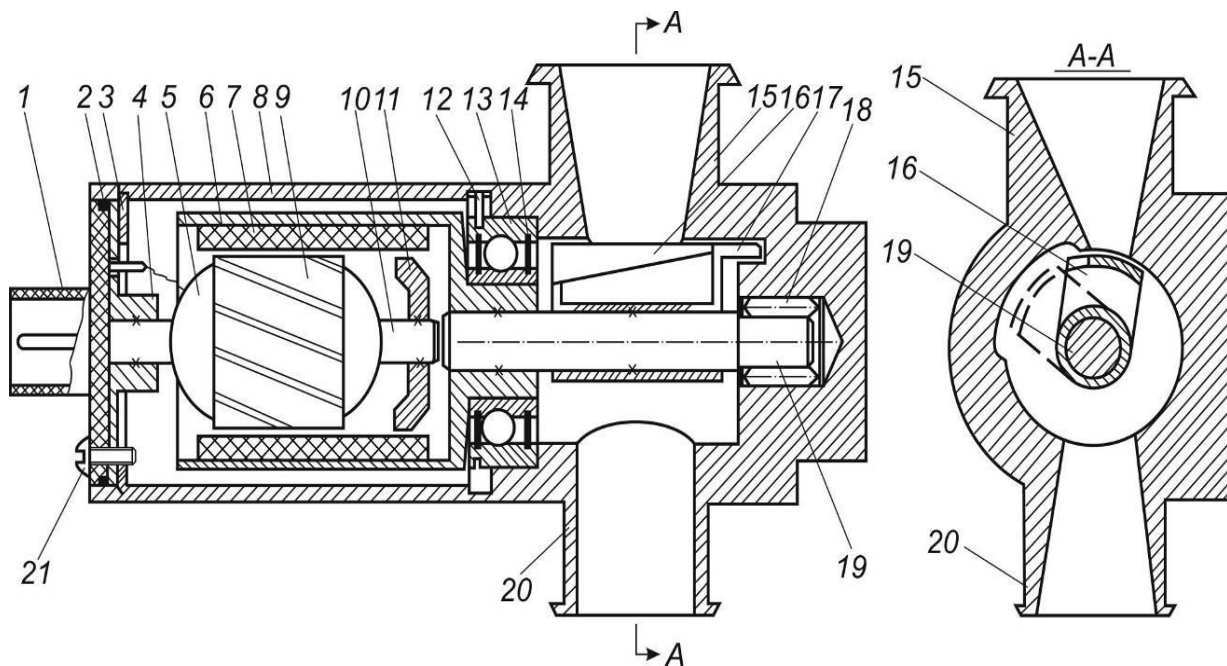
Повздовжній і поперечний вигляд електромагнітного регулятора подачі газу для дизеля з насос-форсунками механічного типу: 1 – штекерна колодка; 2 – кільце ущільнювача; 3 – шайба кріплення; 4 – фланець кріплення осі якоря; 5 – обмотка якоря; 6 – поворотний стакан; 7 – постійний магніт; 8 – корпус; 9 – якір нерухомий; 10 – вісь якоря; 11 – магнітопровід; 12 – стопорне кільце підшипника; 13 – кульковий підшипник; 14 – ущільнення підшипника; 15 – патрубок вхідний; 16 – поворотна заслінка; 17 – упор; 18 – роликовий підшипник; 19 – вал заслінки; 20 – вихідний патрубок; х – з'єднання нероз'ємне
